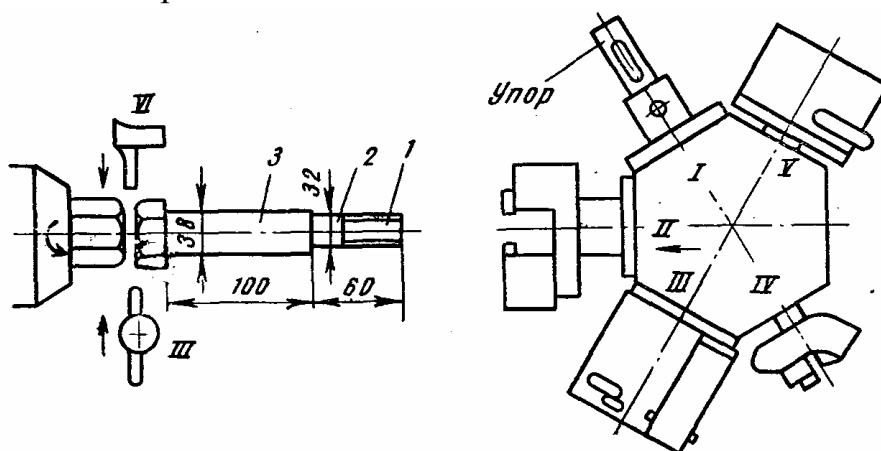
Наладка головки револьверного станка типа *I* для обработки болта из шестигранного прутка
